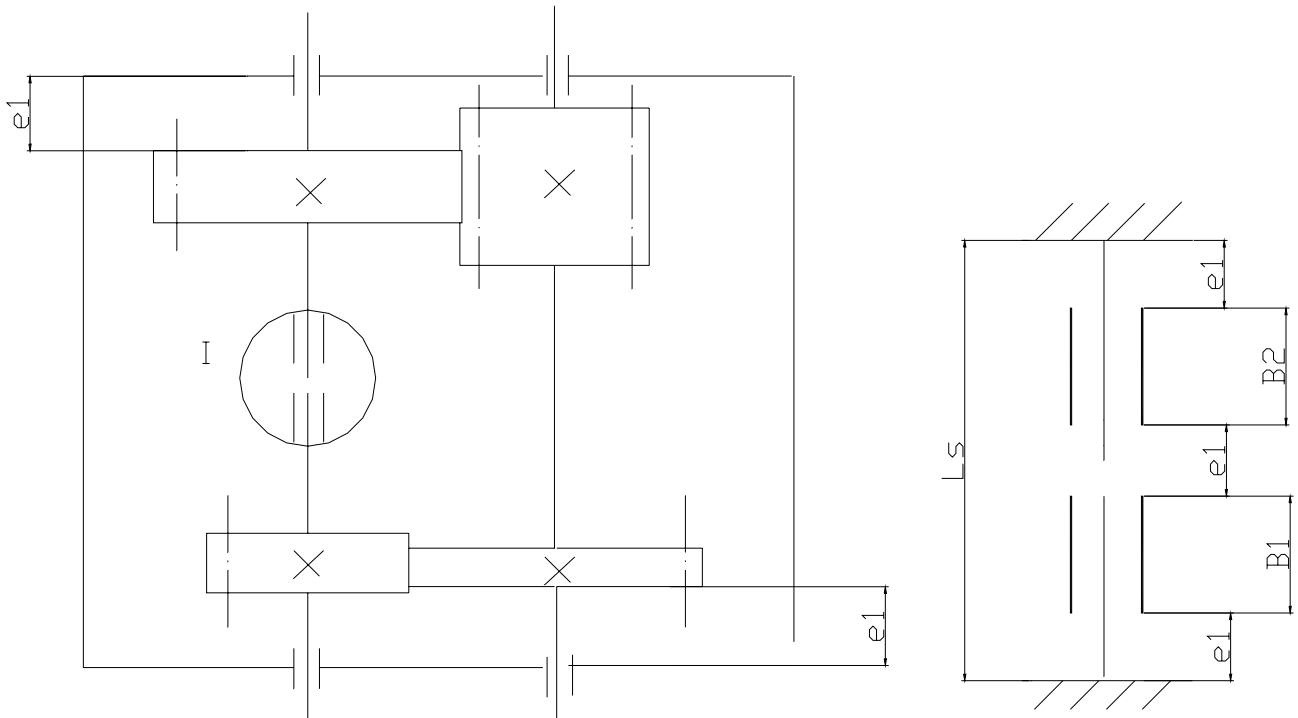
Двухступенчатый редуктор с соосной схемой
